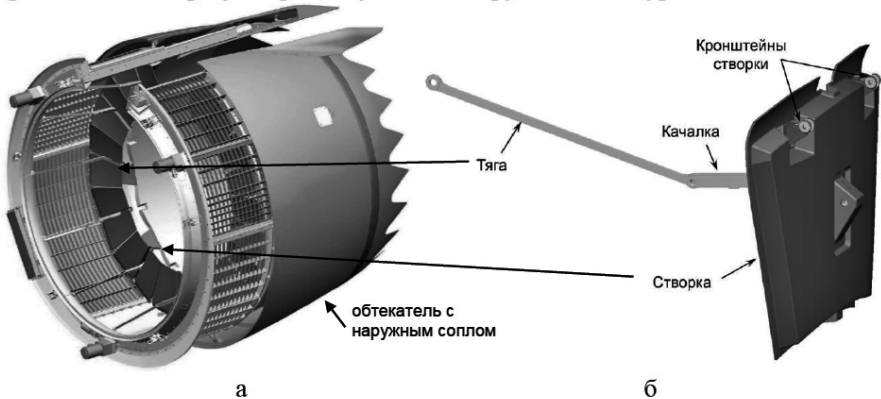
Реверсивное устройство в положении обратная тяга (а) и створка РУ в положении обратная тяга
